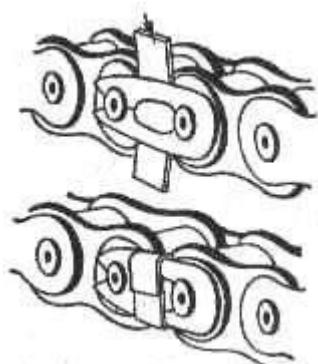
Установка предохранительной полоски из жести на защелку замкового звена цепи
